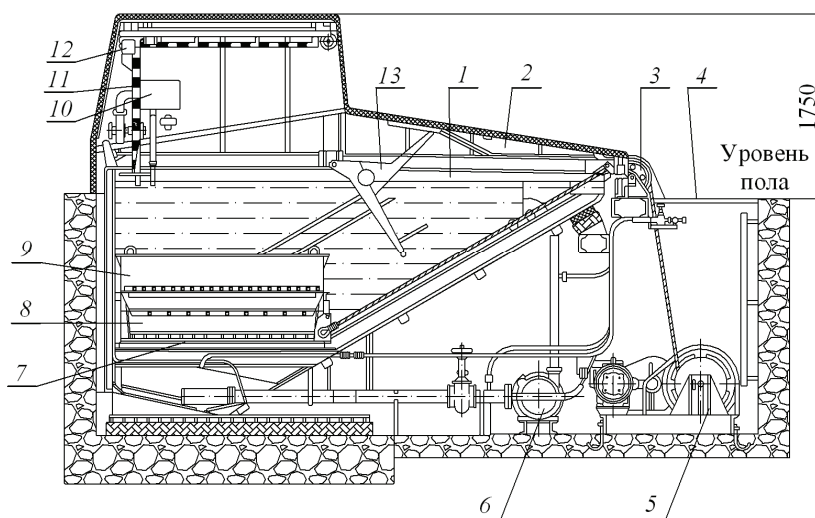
Общий вид электрогидравлической установки модели 36121А: 1 – рабочий бак; 2 – кожух; 3 – блок со стопорным устройством; 4 – лебедка; 5 – крышка фундамента; 6 – система шламоудаления; 7 – тележка; 8 – поддон; 9 – контейнер; 10 – разрядник; 11 – механизм вертикального перемещения; 12 – механизм горизонтального перемещения; 13 – механизм подъема кожуха
